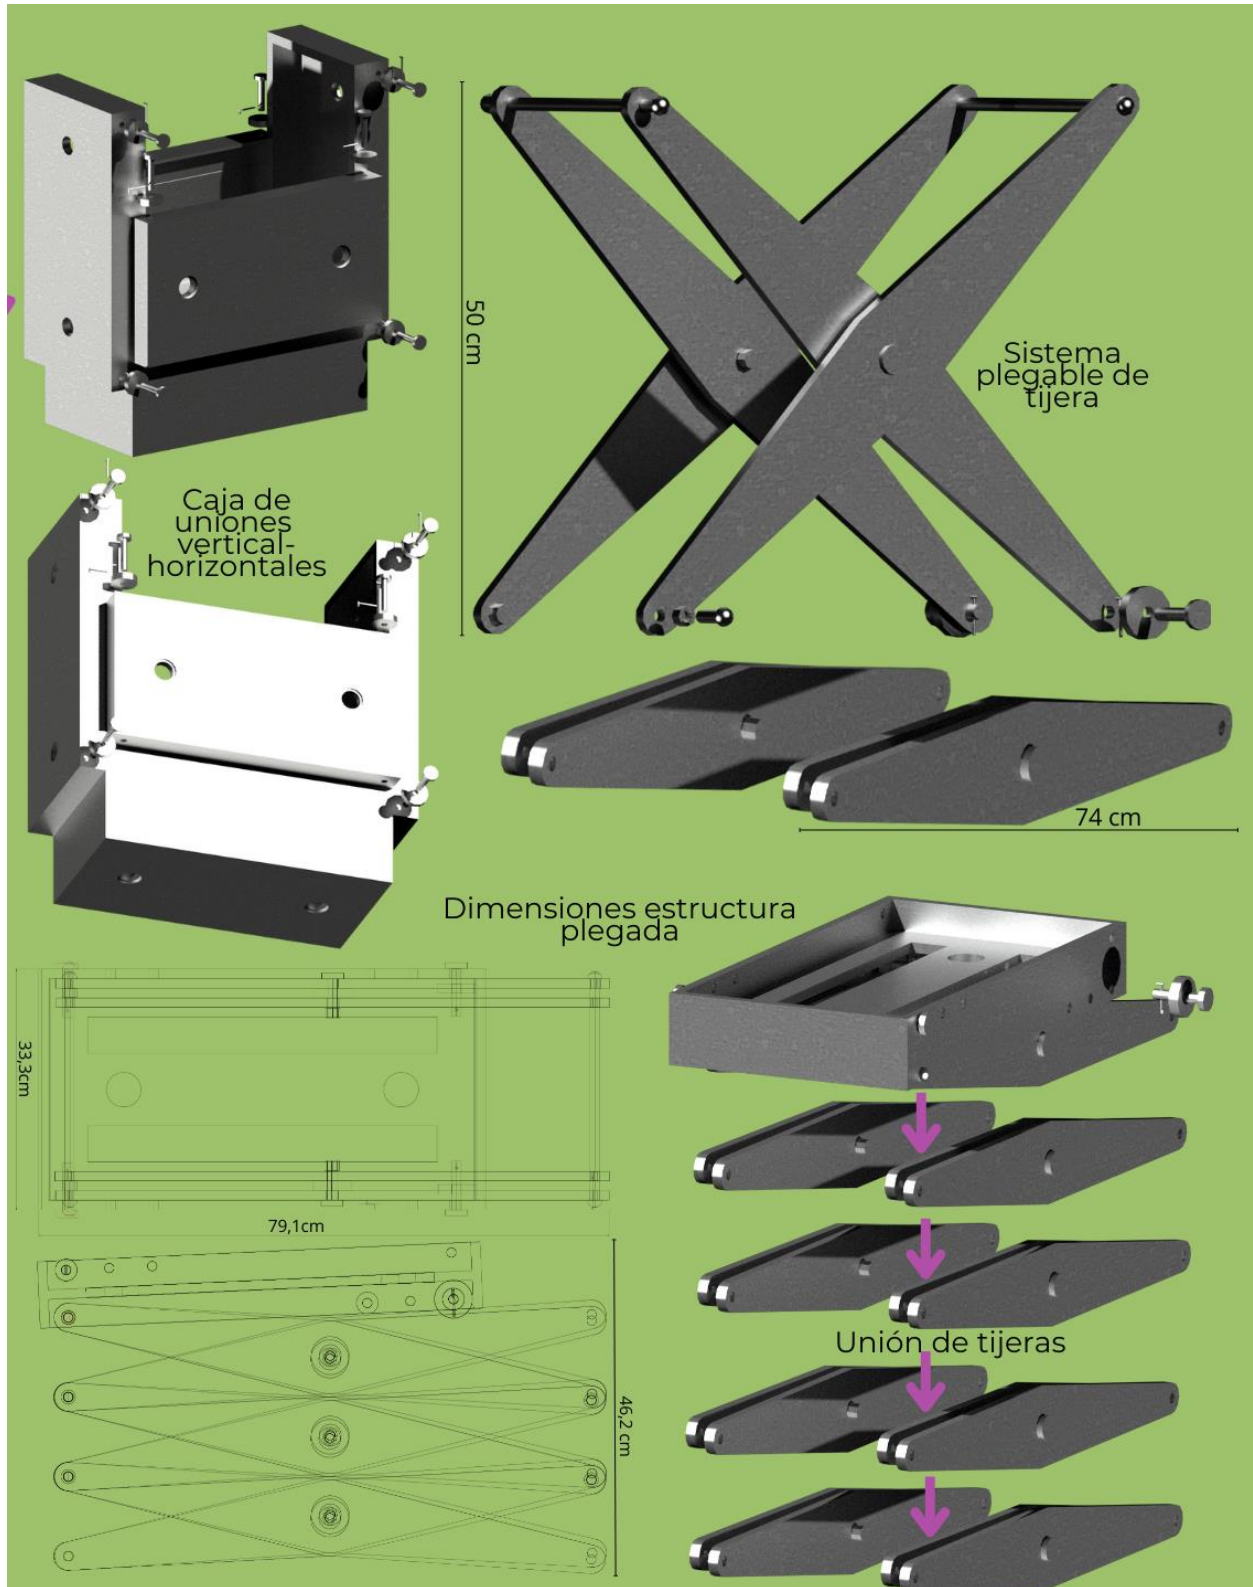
Funcionamiento módulos plegables tipo truss-uniones
